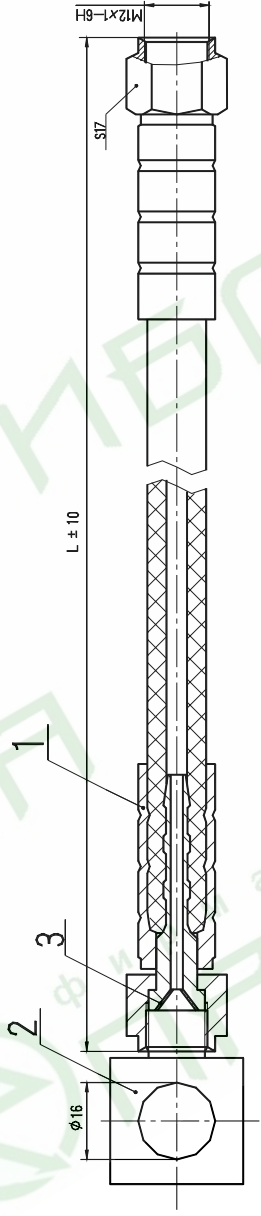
Габаритные и присоединительные размеры шланга ШГ - 15:
